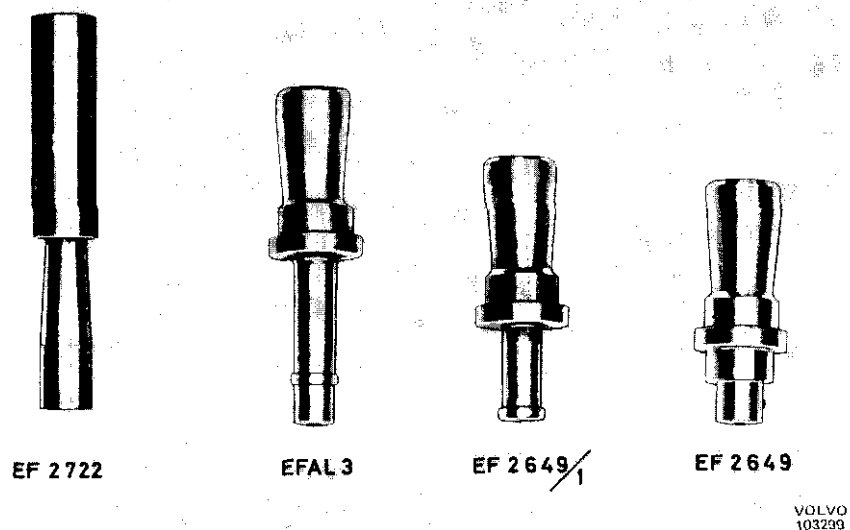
Bosch-Spezialwerkzeuge für Anlasser
